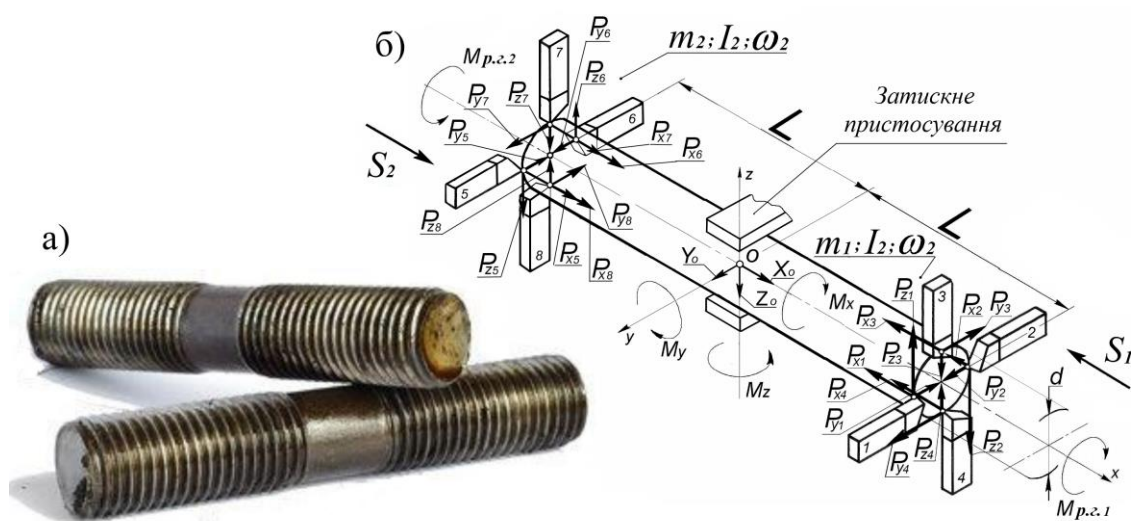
а) Загальний вигляд різьбової шпильки; б) Розрахункова схема нарізання різьби на нерухомій заготовці різьбовими головками з вісьмома ріжучими елементами.
